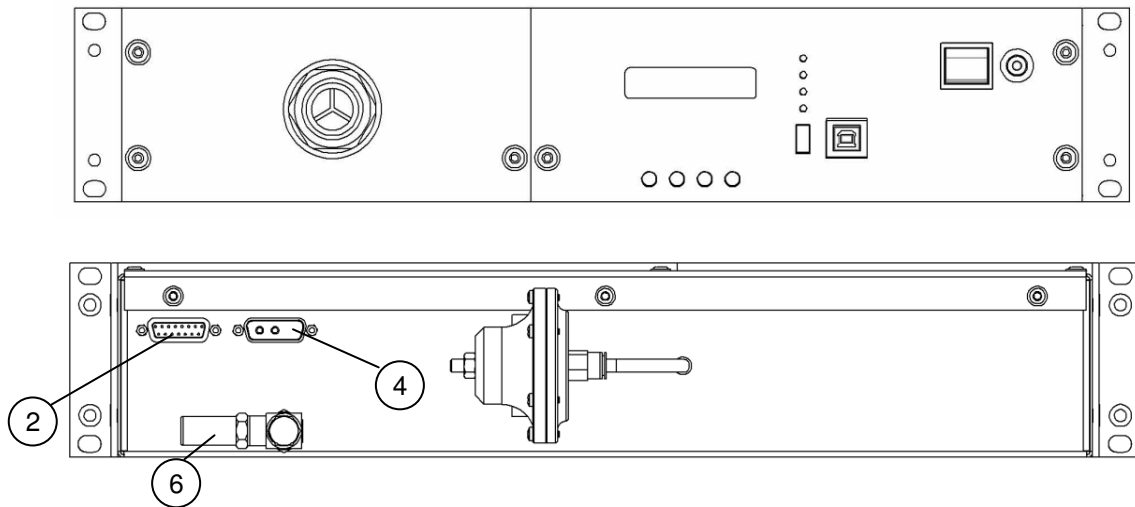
Bedienelemente (Sonderausführung 2HE)
